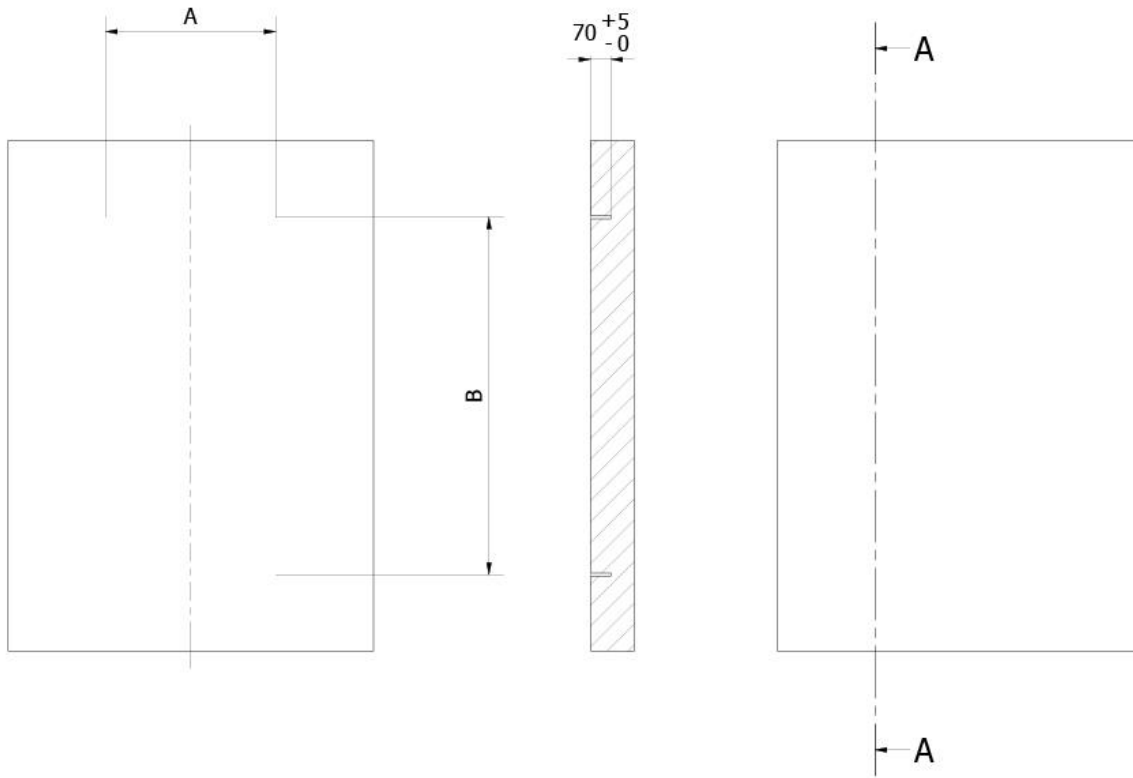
Dimensions des ouvertures pour les éléments de montage standard
